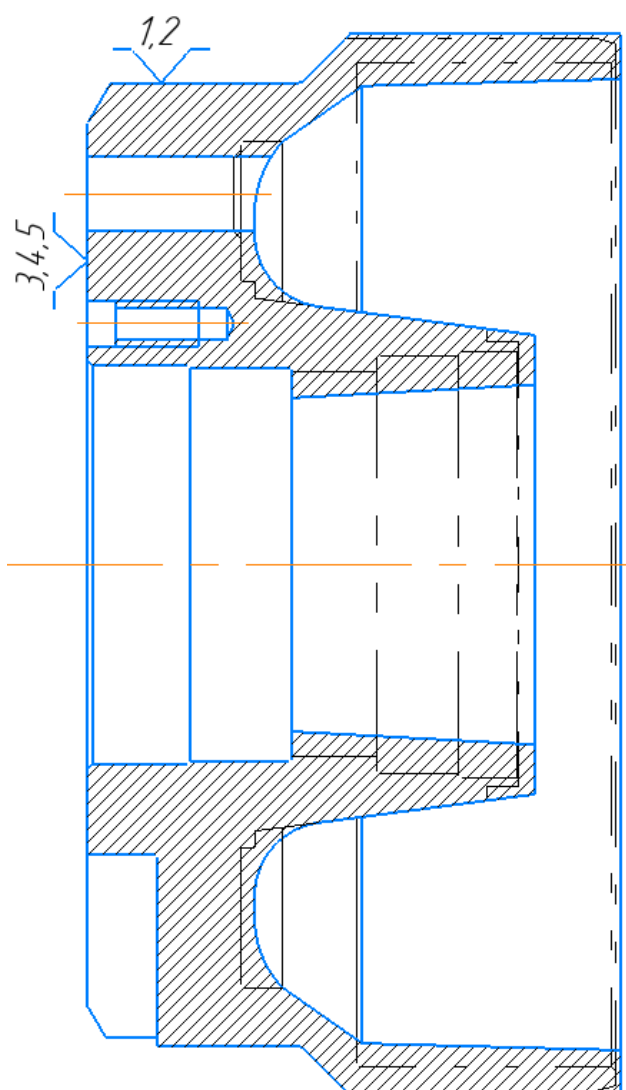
Базирование детали при установе Б в трехкулачковый патрон
